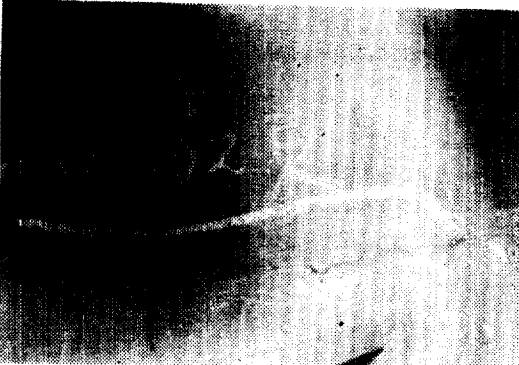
그림 7 "F" I Beam 용접부 CRACK
